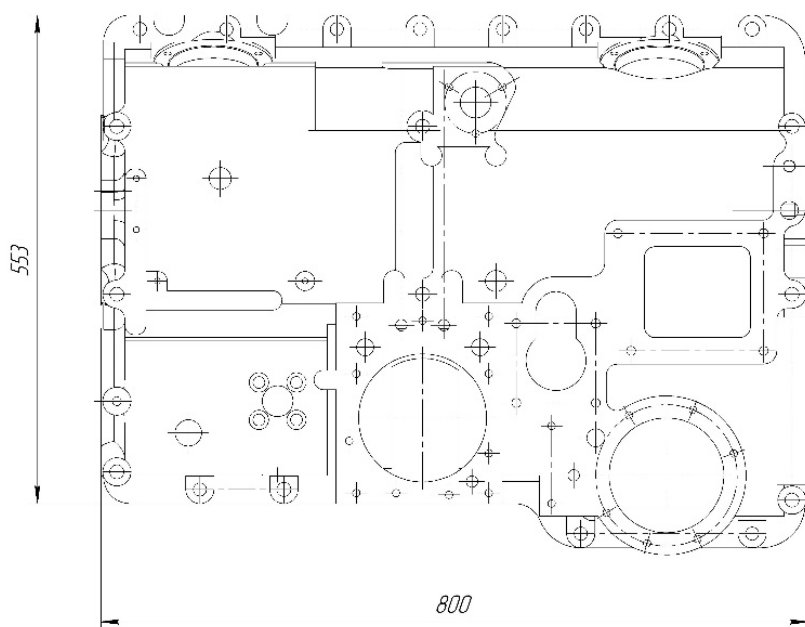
Габаритные размеры картера КПП верхней половины
